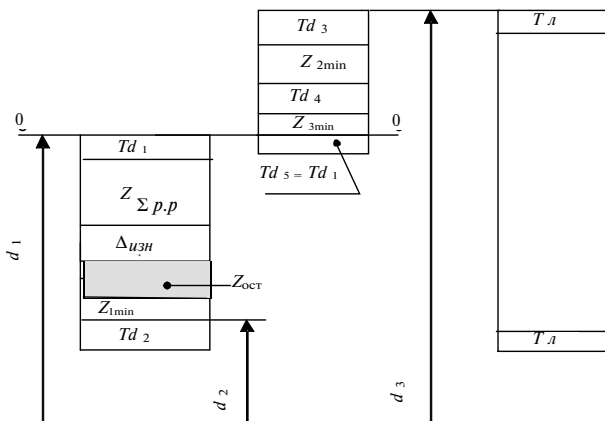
Схема полей припусков и допусков на обработку резанием восстанавливаемых шеек коленчатых валов:
